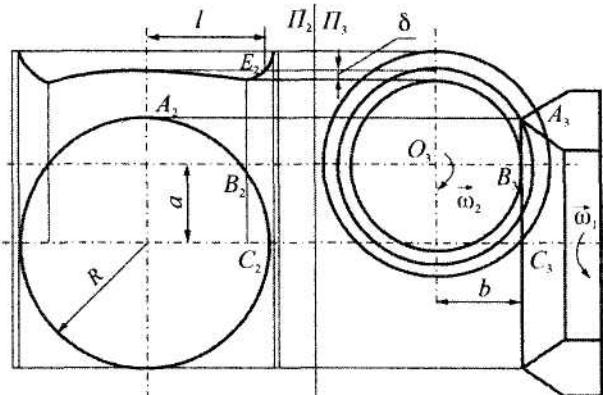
Схема формоутворення круглої циліндричної поверхні торцевою фрезою
